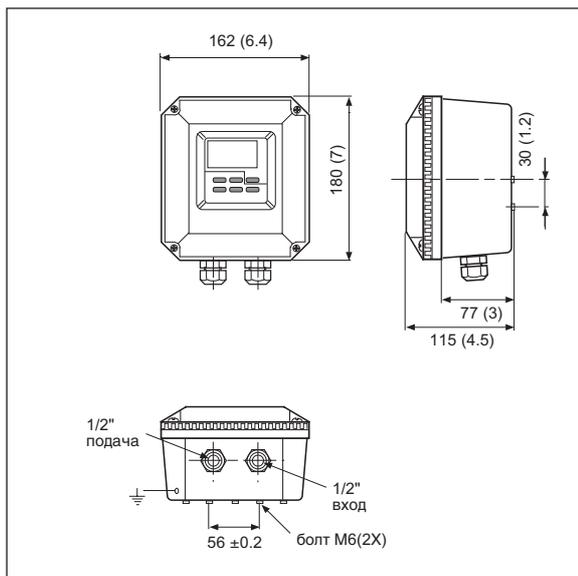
Размеры корпуса и схема установки кабельных уплотнителей
